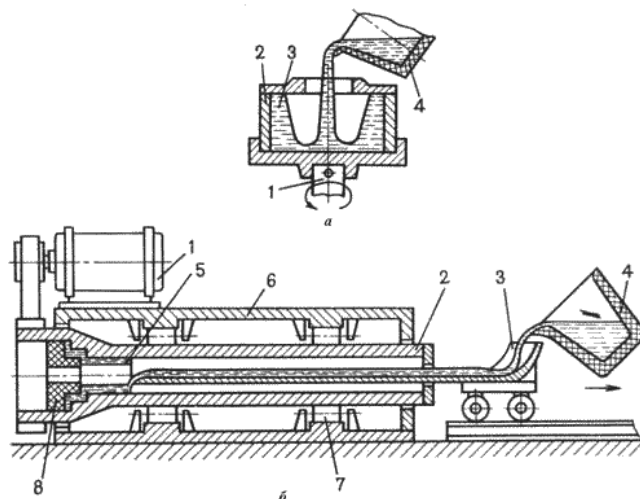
Схемы процессов изготовления отливок центробежным литьем
